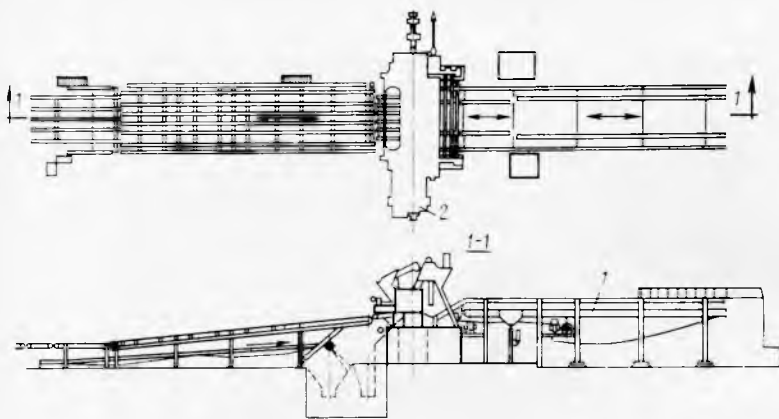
Линия лущения — рубки — укладки шпона: 1 — транспортер для подачи чурakov; 2 — лущильный станок
